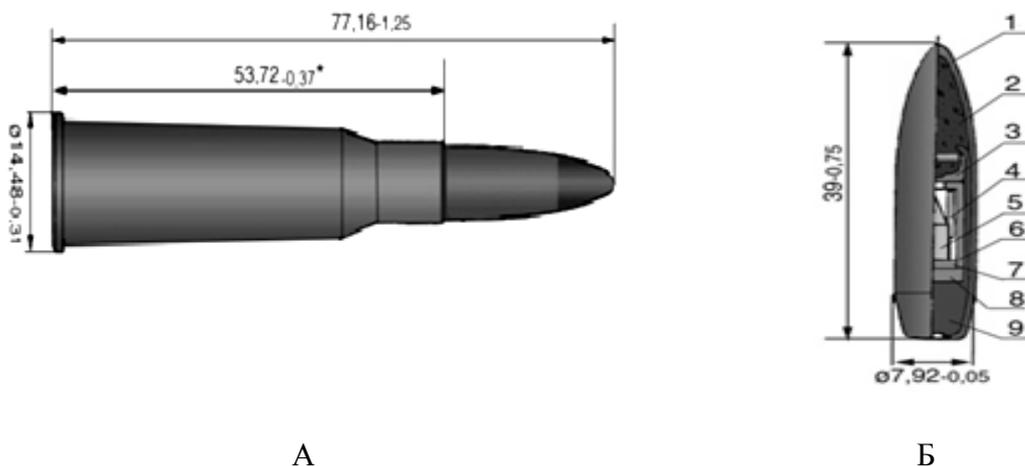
7,62-мм винтовочный патрон с пристрелочно-зажигательной пулей:
